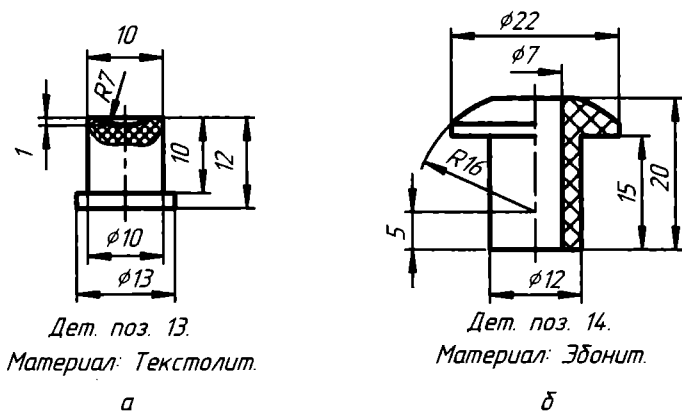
Чертежи: а — кнопки; б — втулки
